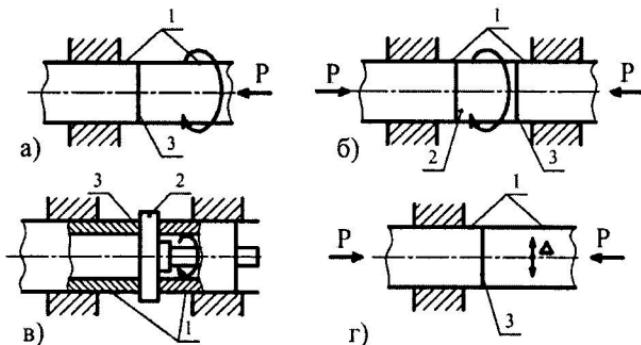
Схеми процесу зварювання тертям: 1 – деталі, що зварюються; 2 – вставка; 3 – зона зварювання
